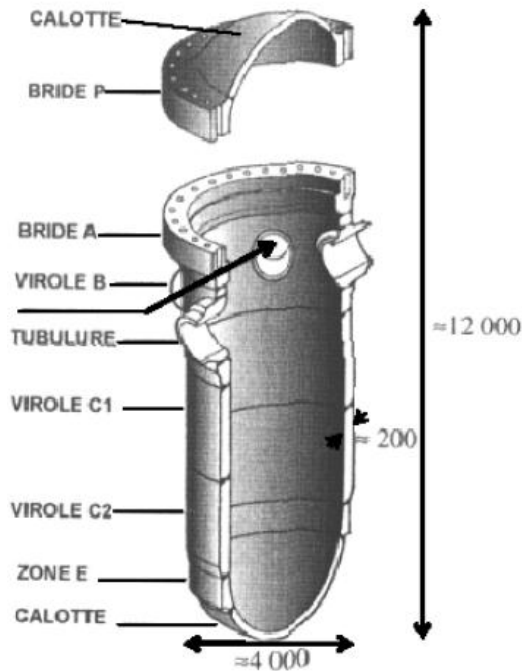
Vue en coupe d'une cuve de réacteur à eau sous pression indiquant les principales pièces et dimensions (en mm) [Carassou 2000].
